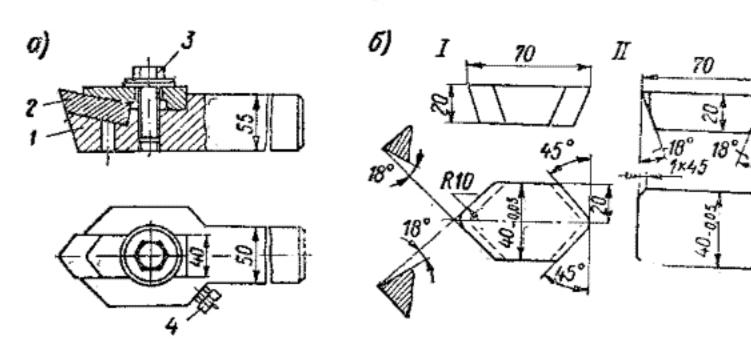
Многокромочный резец с механическим крепление режущей пластинки.
